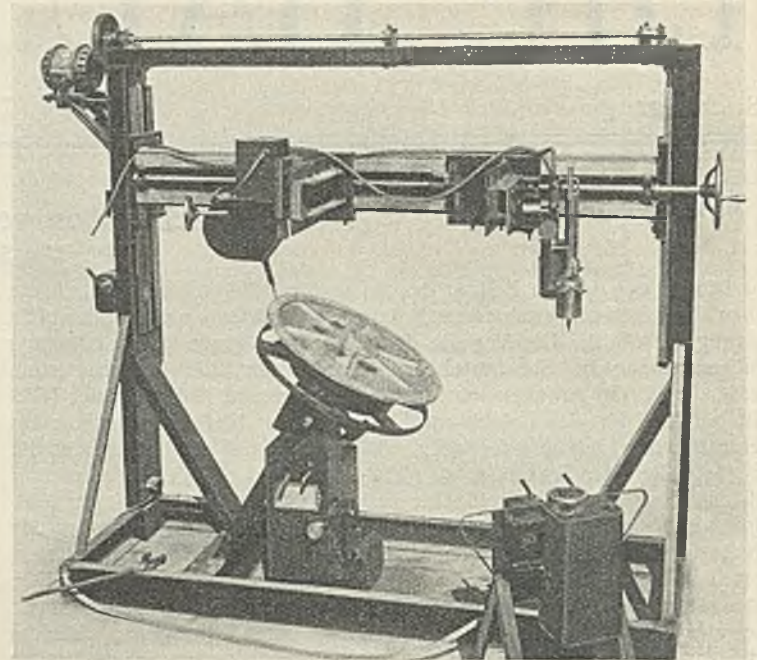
Schweißmaschine der AG. Elin.
